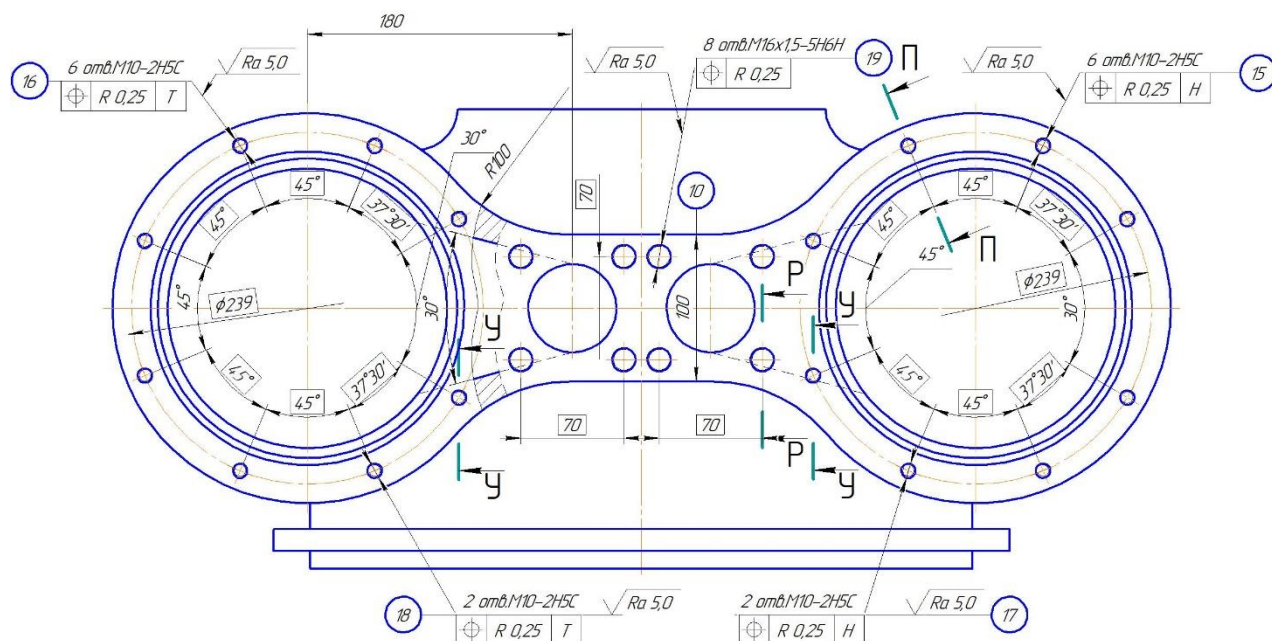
Вид Г. Нумерация поверхностей детали «Корпус охладителя»
